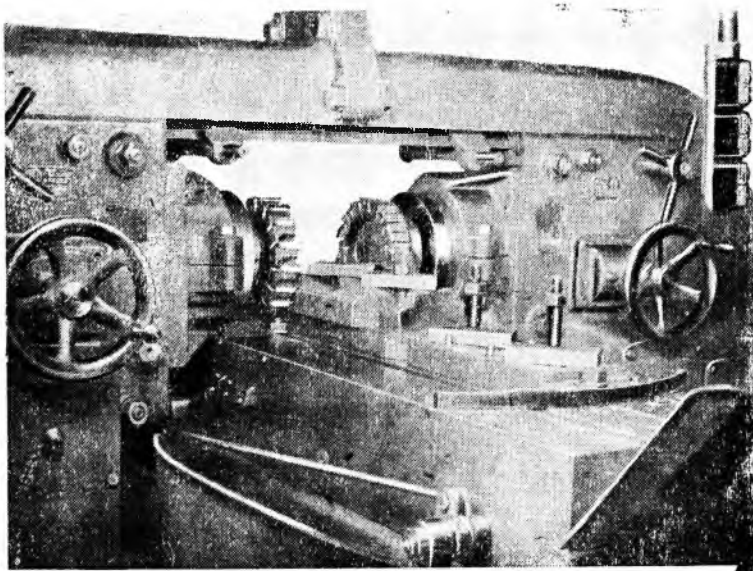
Фрезерование верха, профиля и боковой плоскости рамки набором фрез
